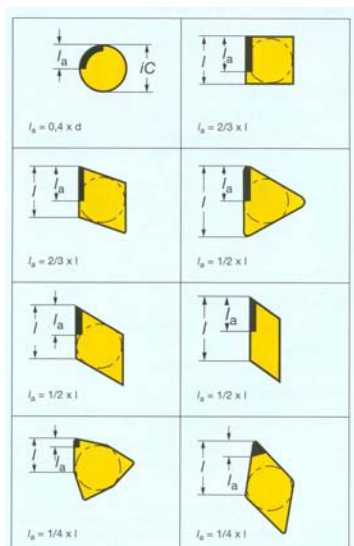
Cálculo de comprimento efetivo da aresta de corte (adaptado da referência [15])
